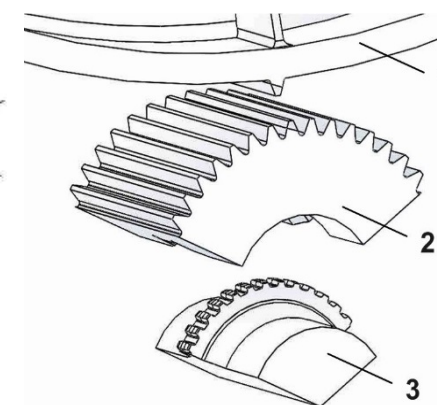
Геометрическая модель зубчатого зацепления с самоустанавливающейся шестерней: 1 – венец барабана; 2 – венец шестерни; 3 – вал шестерни
